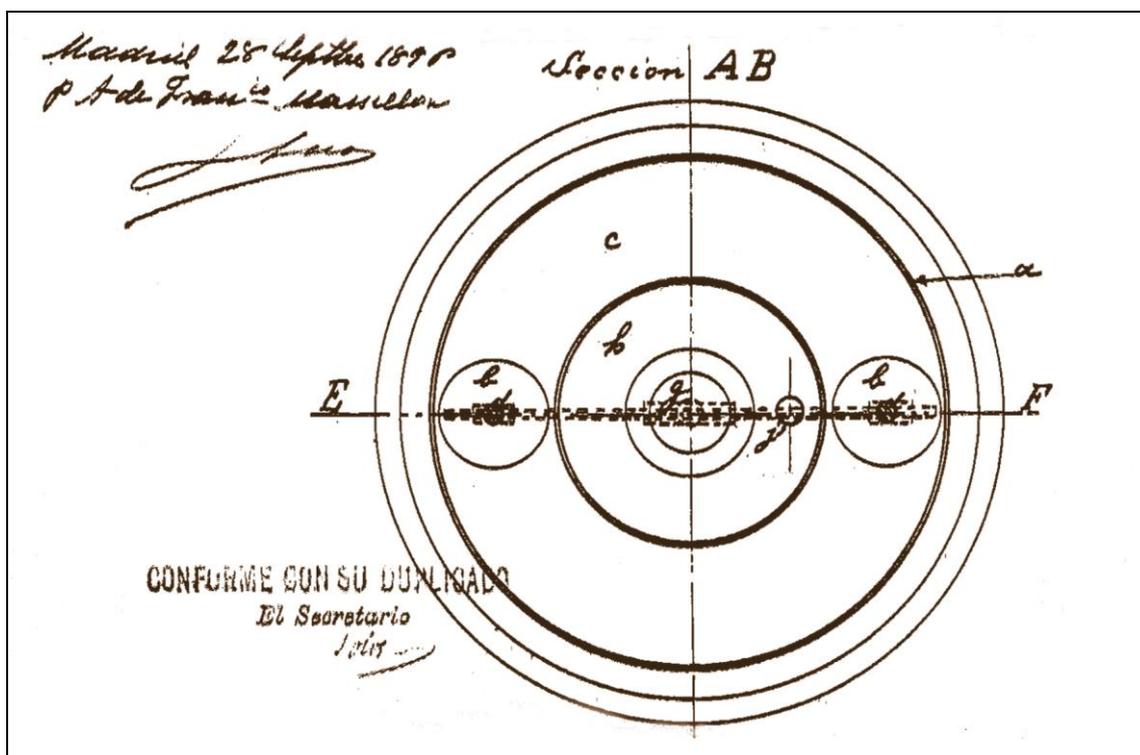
Vista en planta inferior del aparato (Arch. J.M. Sanchis)
